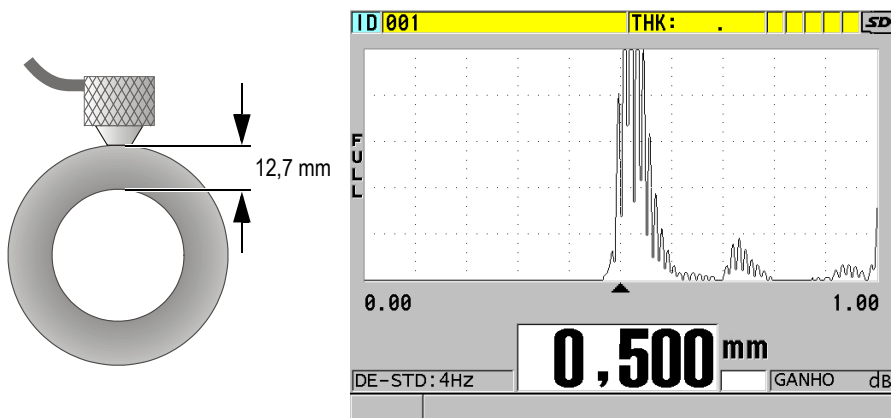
Acoplamento de transdutor de elemento duplo e leitura da medição de espessura
